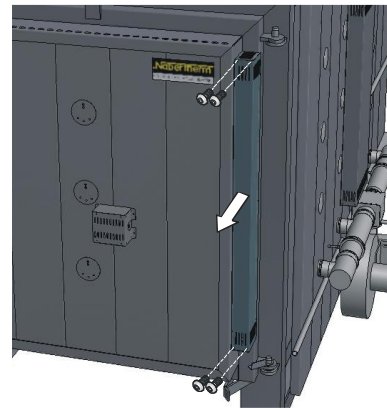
Przykład: Montaż elementów grzewczych (ilustracja pogładowa)
